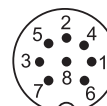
Pinbelegung S32 (Draufsicht auf Stecker am Wegaufnehmer), 8-poliger Rundstecker M16
